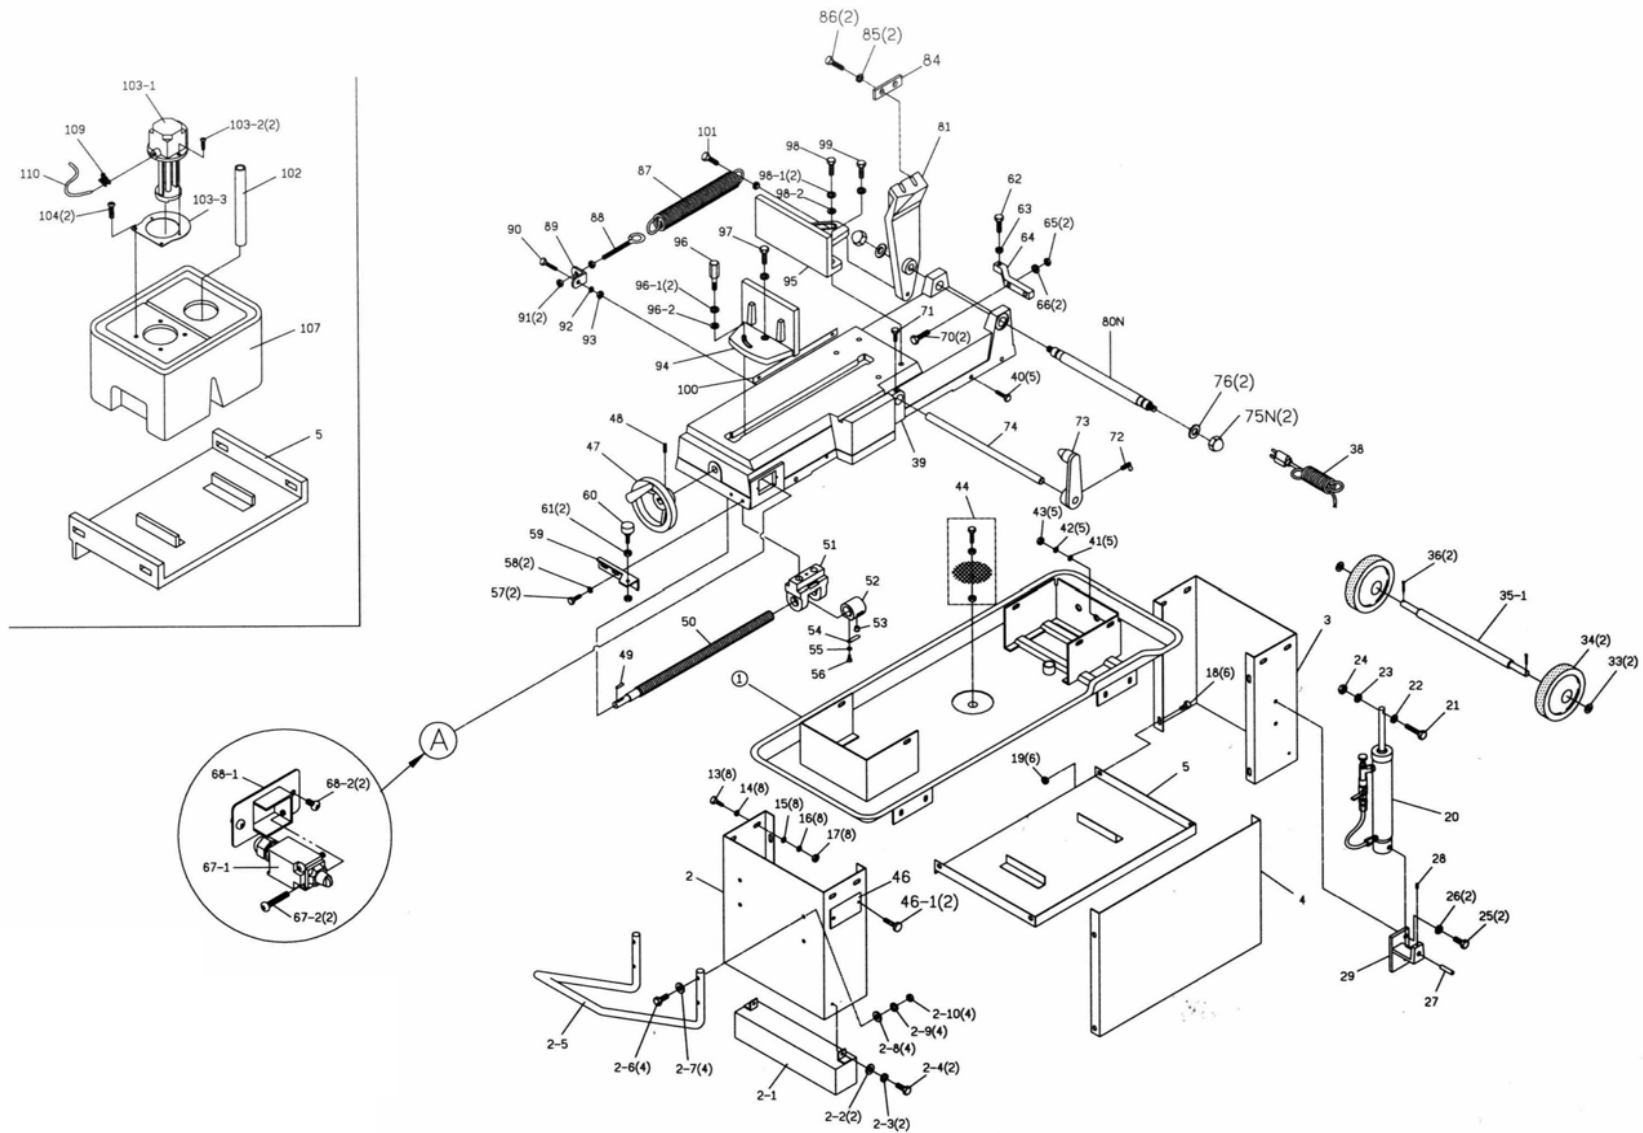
Explosionszeichnung 1 - Explosion drawing 1 S181
